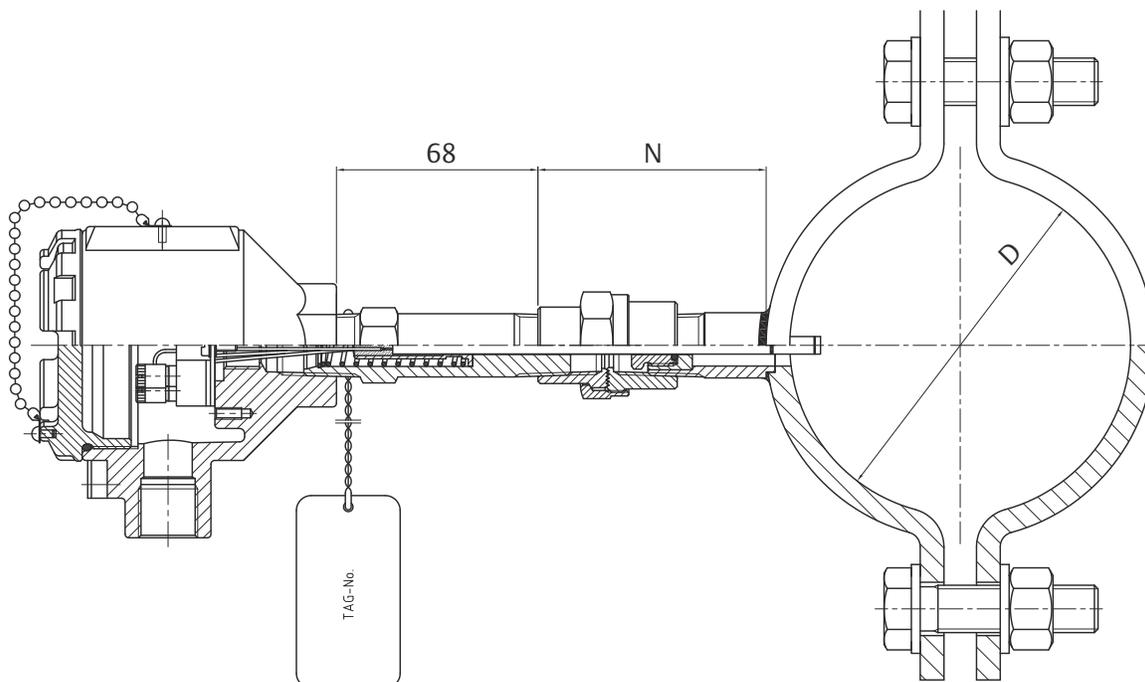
Универсальный монтаж на трубе с соединительной головкой Rosemount
